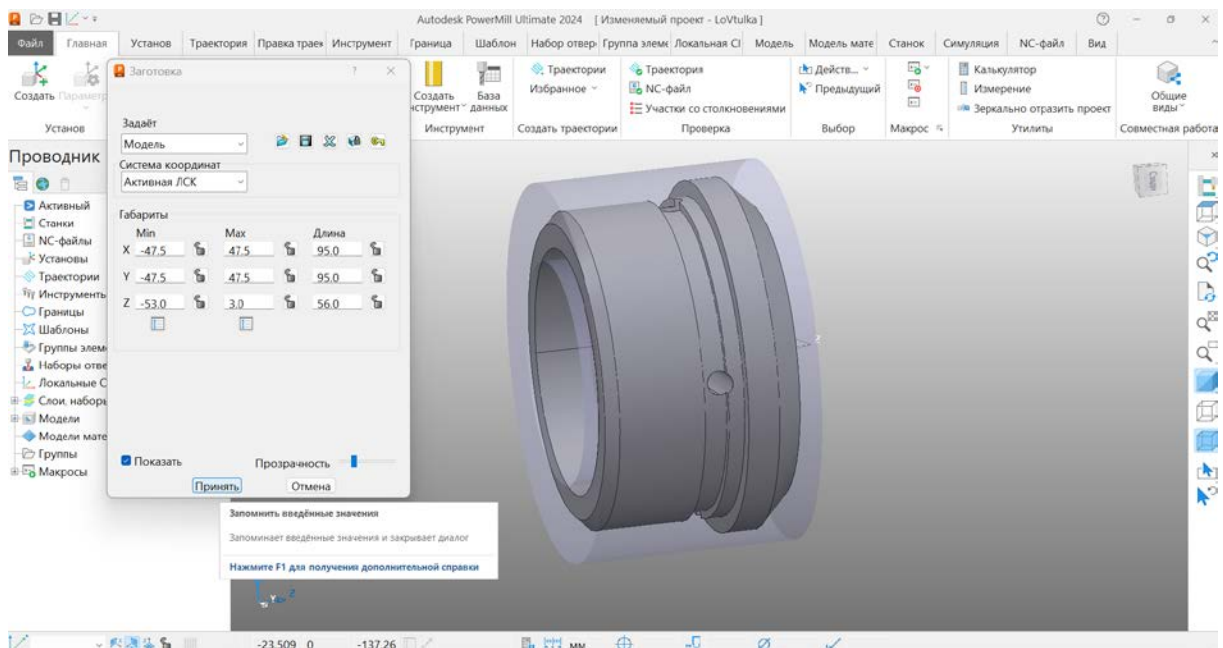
Імпортовані моделі деталі та заготовки
